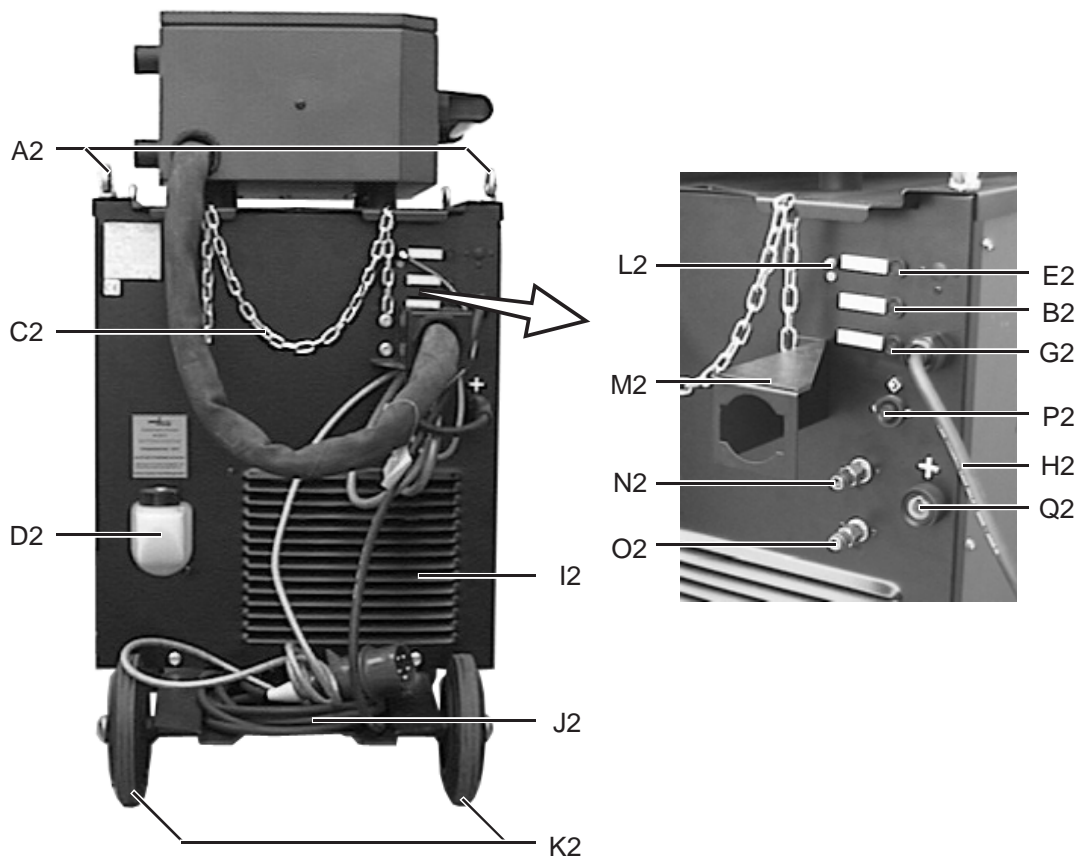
/4; Rückansicht (dekompakte Ausführung)
